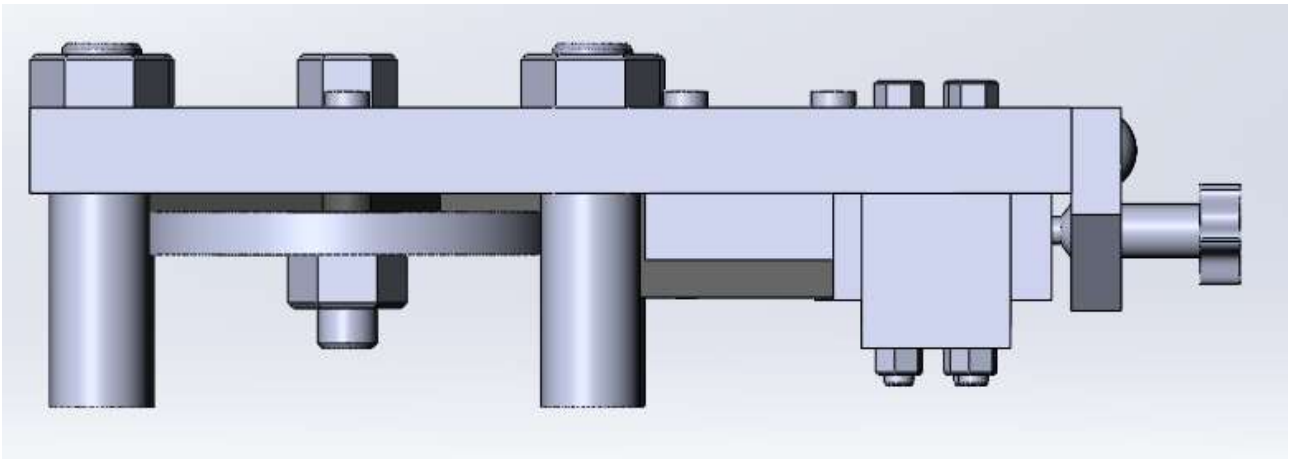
Верстатний пристрій (Вид з боку)
